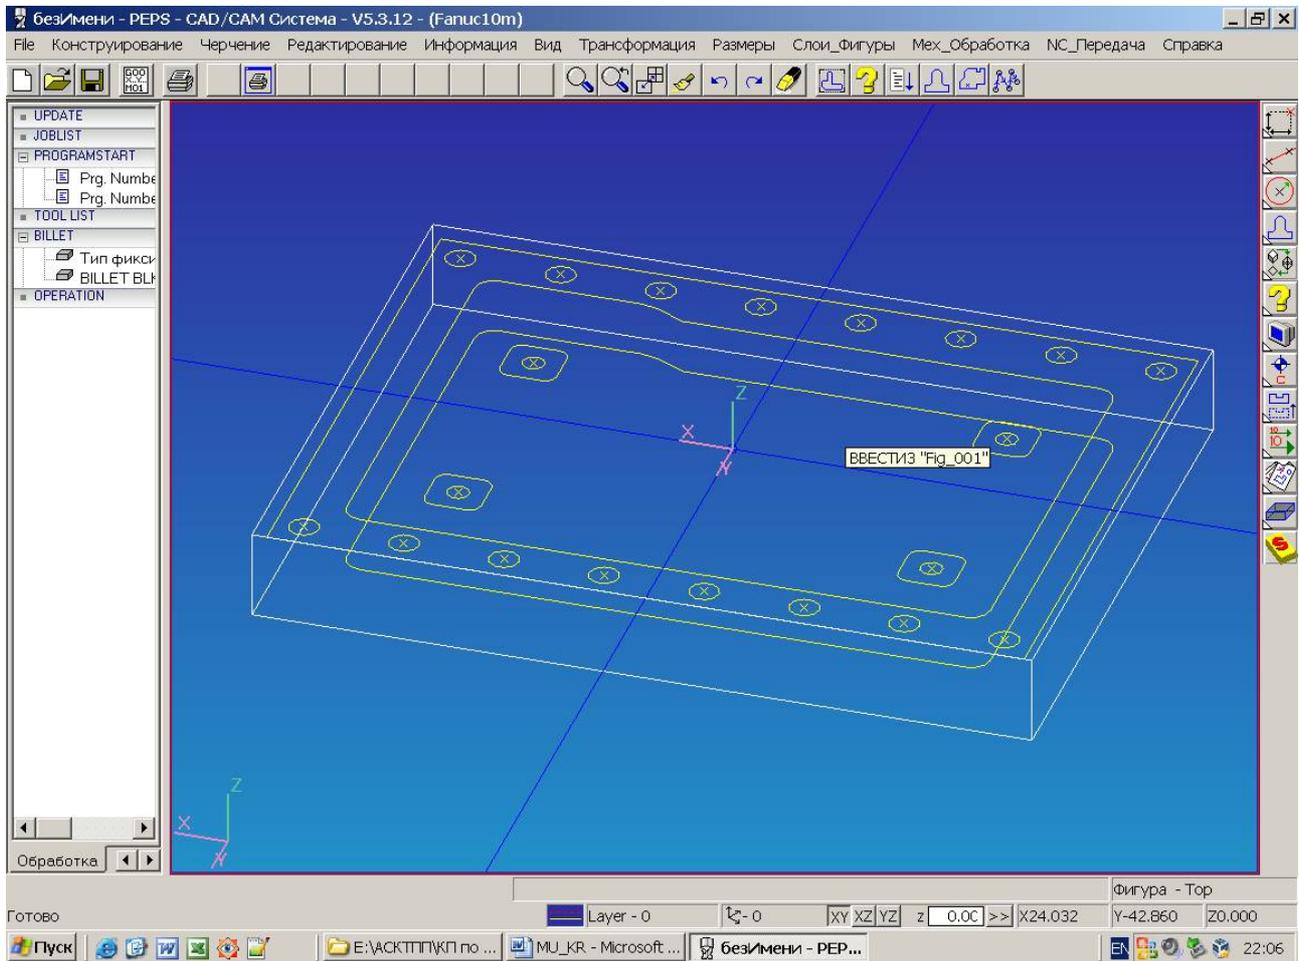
Вид заготовки и обрабатываемых контуров
